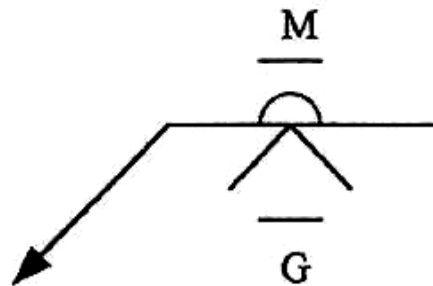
SÍMBOLOS DE PERFIL ENRASADO POR MEDIO DE ESMERILADO POR EL LADO FLECHA, Y MAQUINADO POR EL OTRO LADO DE LA FLECHA, EN LA SOLDADURA DE RESPALDO.
